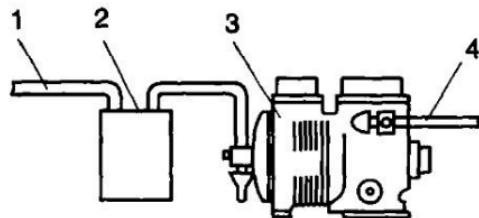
Схема монтажа отделятеля жидкости на всасывающем трубопроводе:
